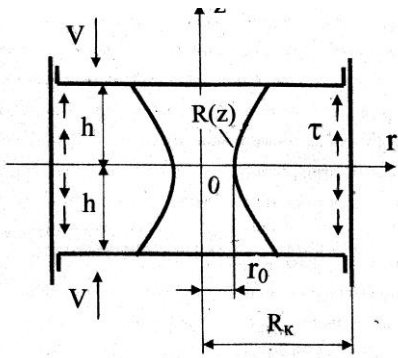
Схема осадки полой цилиндрической заготовки в пресс-форме
